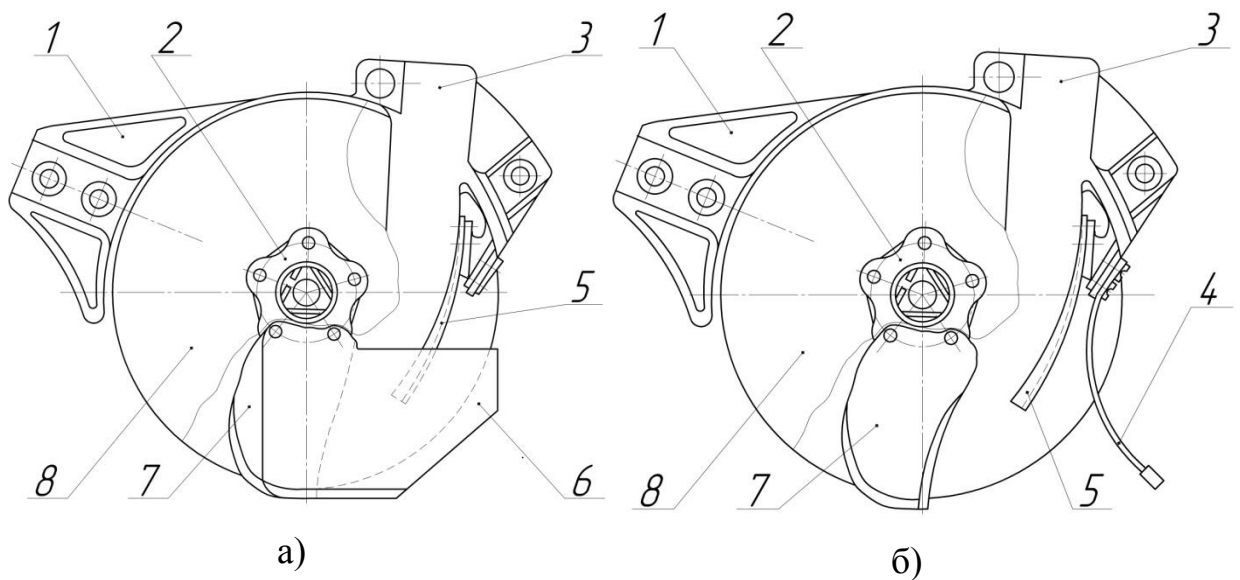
Дводисковий сошник: а) з п'яткою та напрямником; б) з п'яткою та прутками загорточачи; 1 – корпус; 2 – маточина; 3 – лійка; 4 – прутки загорточач; 5 – напрямник; 6 – щоки; 7 – п'ятка; 8 – диски
